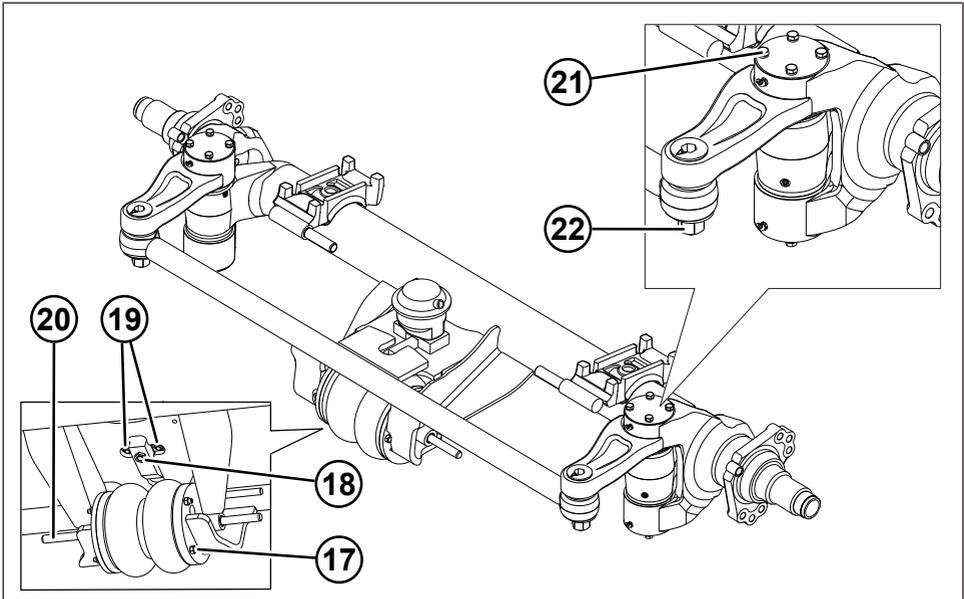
Vue d'ensemble des couples de contrôle et de serrage Essieu suiveur
